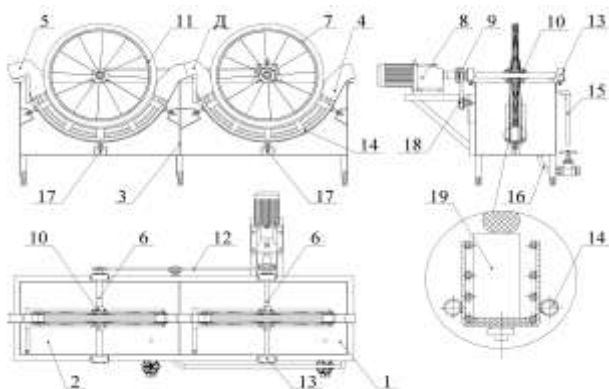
Схема моечной машины для наполненных металлических цилиндрических консервных банок: 1, 2 – ванны моечные; 3 – перегородка; 4, 5 – направляющие; 6 – вал; 7 – колесо ведущее; 8 – мотор-редуктор; 9 – муфта; 10 – ступица; 11 – колесо ведомое; 12 – клиноременная передача; 13 – корпус; 14 – барботер; 15 – патрубок перелива; 16 – патрубок сливной; 17 – крепежно-регулирующая шпилька; 18 – натяжное устройство; 19 – банка консервная
